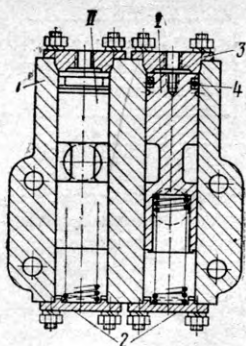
Золотниковая коробка редуктора вспомогательных механизмов:
